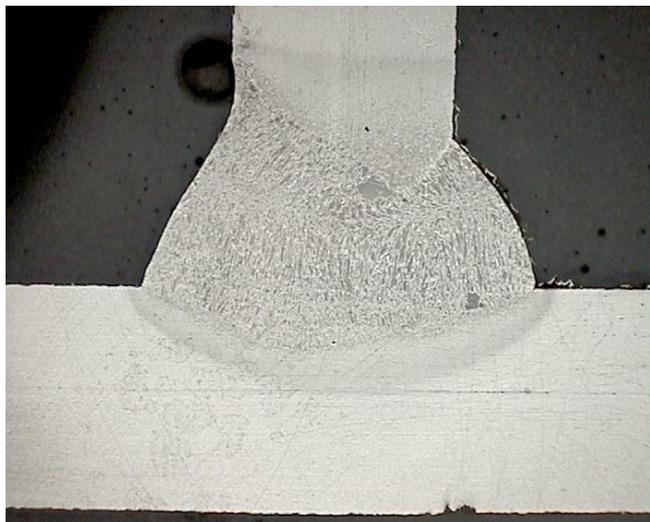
Поперечный шлиф, угловой шов, положение сварки РВ
